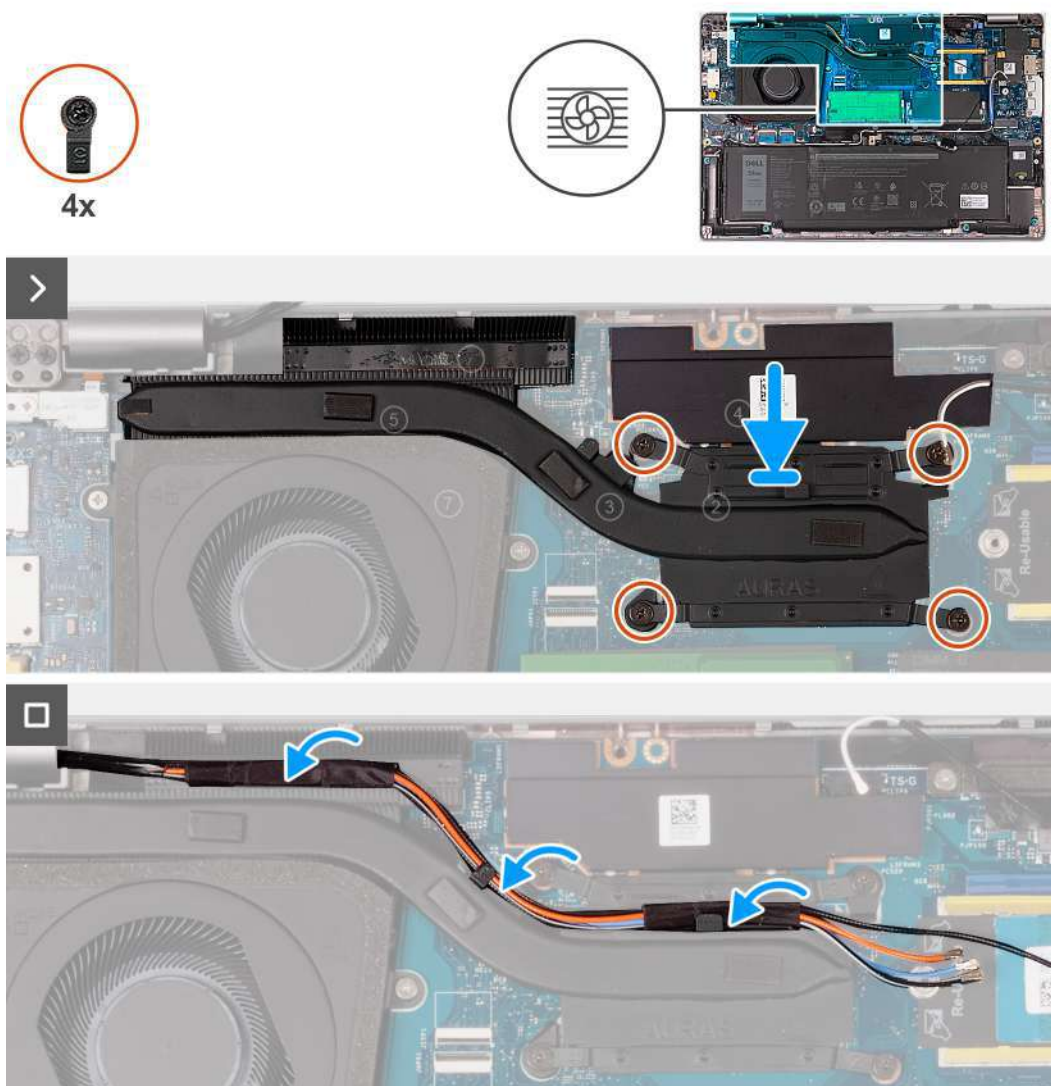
Como instalar o dissipador de calor - computadores com placa 5G
